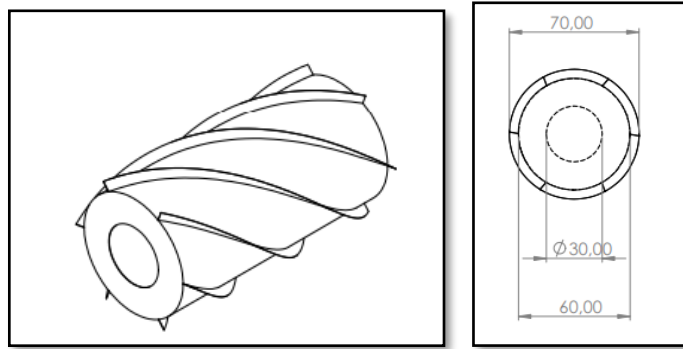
Dimensiones del cilindro interno del intercambiador de calor
